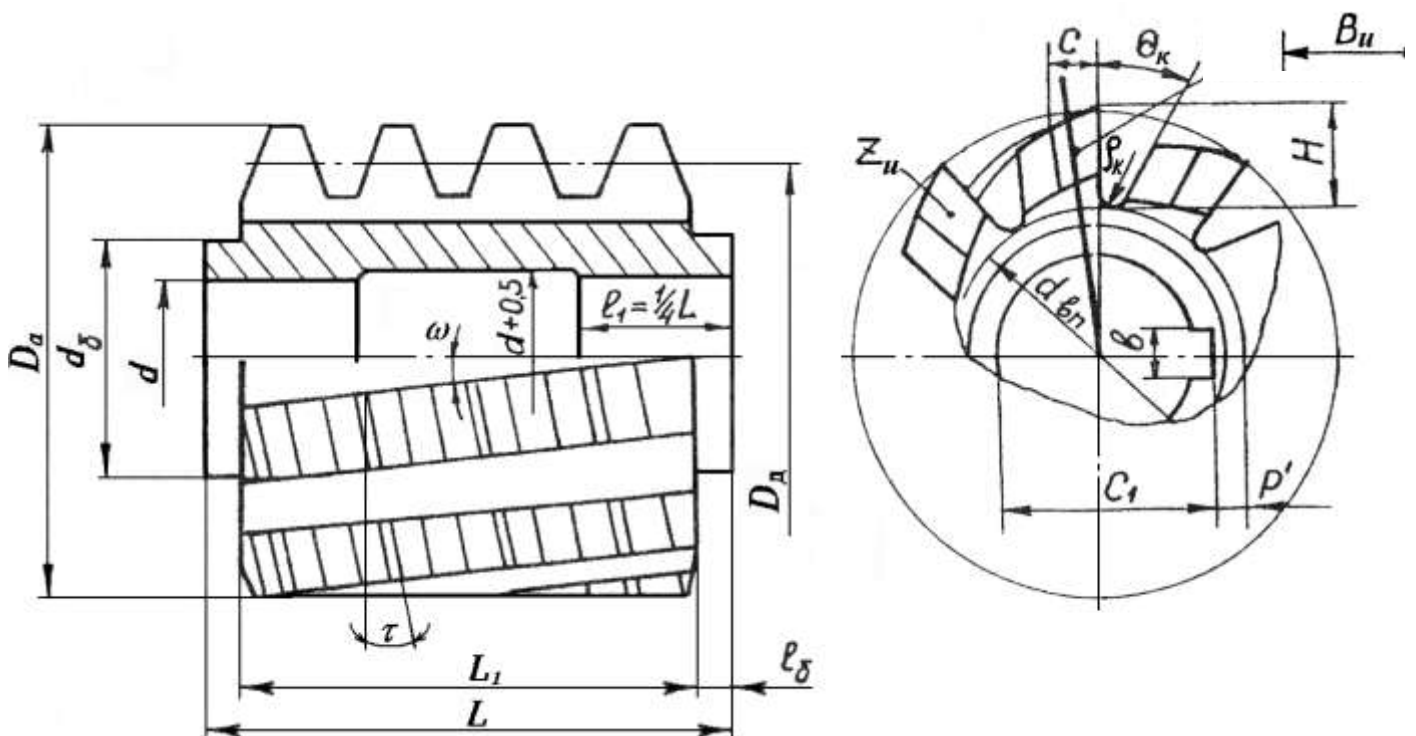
Черв'ячна фреза для обробки циліндричного зубчастого колеса
